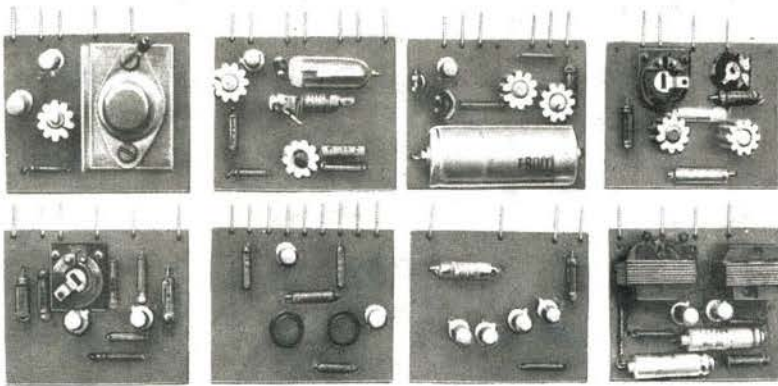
Funktionsblock für die Aufnahme von 20 Baugruppen. Draufsicht mit den Baugruppen für die Schaltung nach Bild 32 bestückt, mit zusätzlichen Baugruppen für Auslösung von Schaltvorgängen durch fahrende Züge
